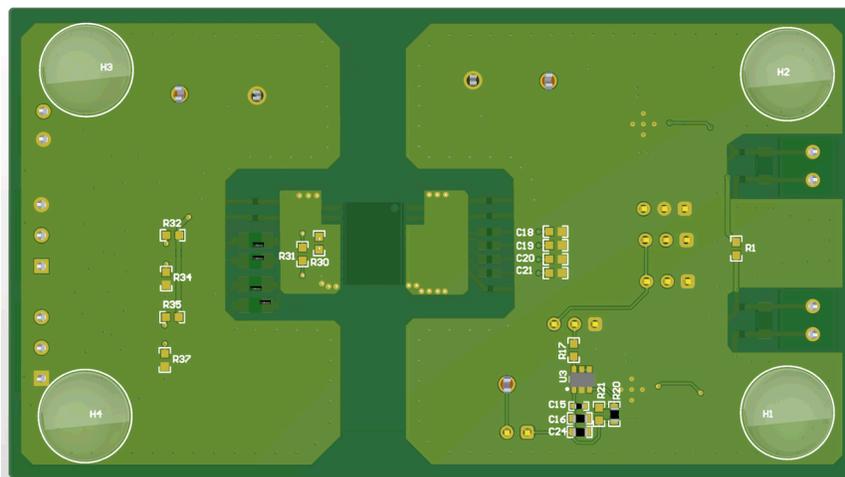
ISOW380DWEEVM PCB 3D 视图 - 底层
